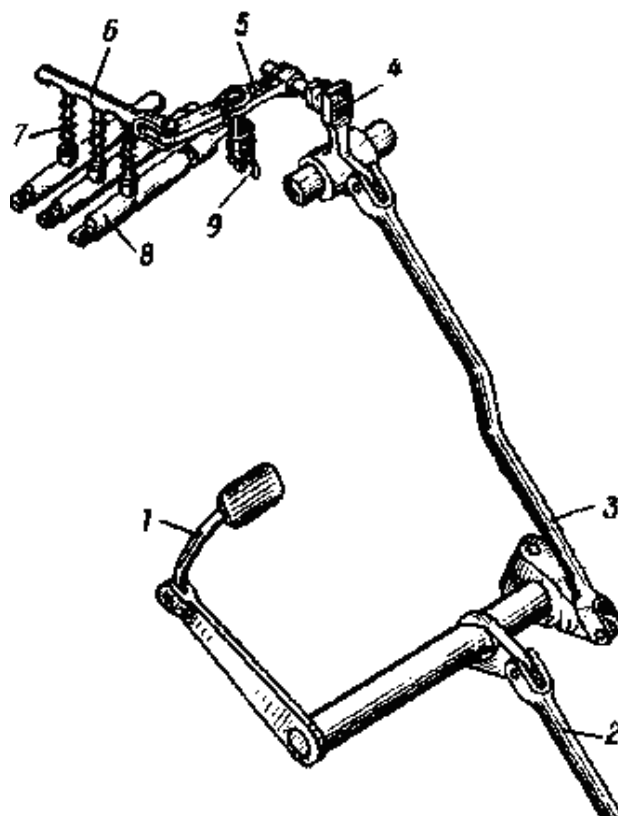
Схема блокировочного механизма привода управления коробкой передач:
